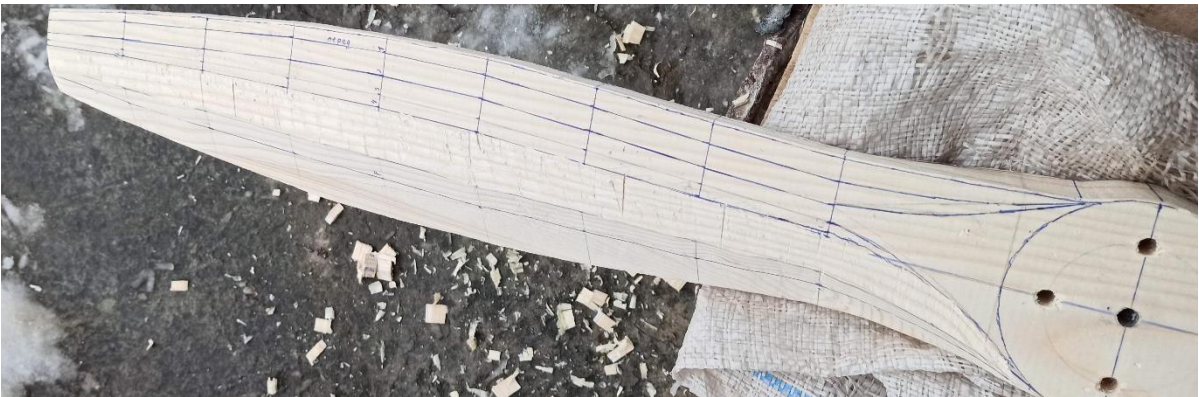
Знятий непотрібний матеріал верхньої частини лопаті
